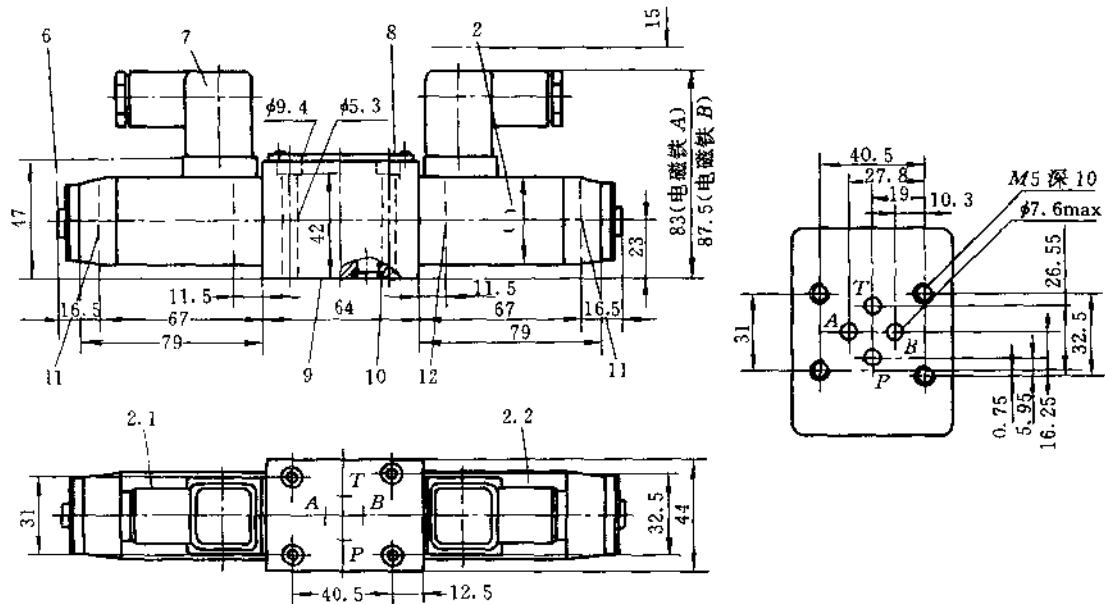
WE6 型电磁换向阀外形与连接尺寸图
